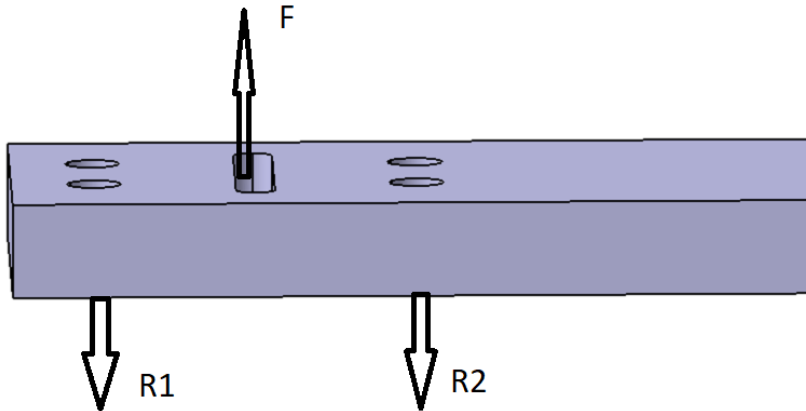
Modelo de fuerzas aplicadas sobre la placa
